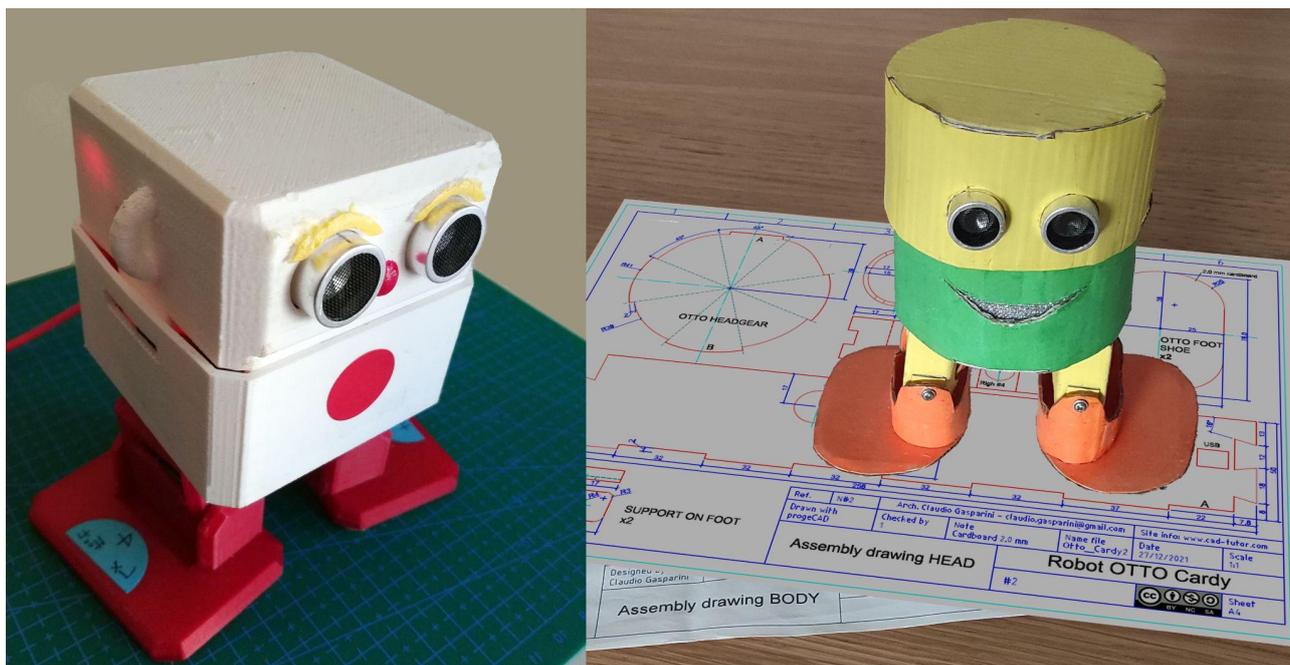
A sinistra OttoDIY realizzato con la stampante 3D e a destra la versione di cartone OttoCardy con i due disegni tecnici forniti per la sua costruzione
